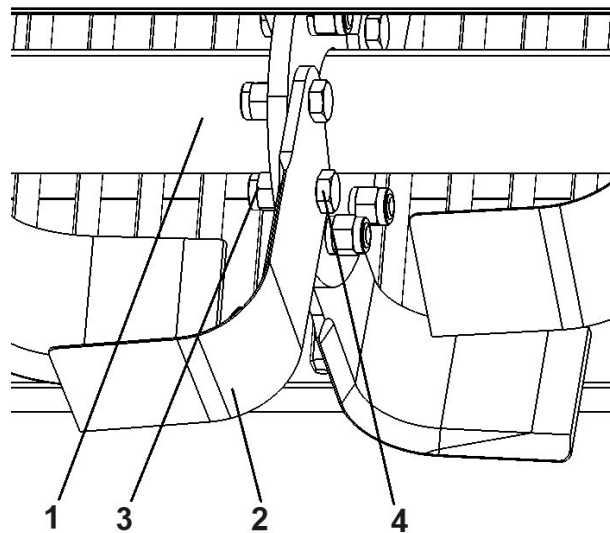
Austausch der Bogenmesser: 1 – Arbeitswelle, 2 – Bogenmesser, 3 – Mutter, 4 – Schraube
